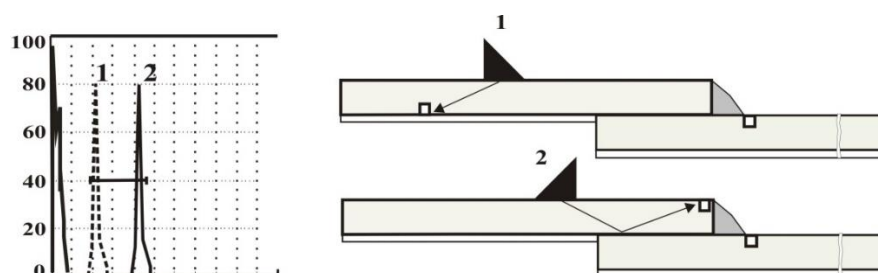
Схема настройки строб-импульса при контроле нахлесточных сварных соединений со стороны верхнего элемента
